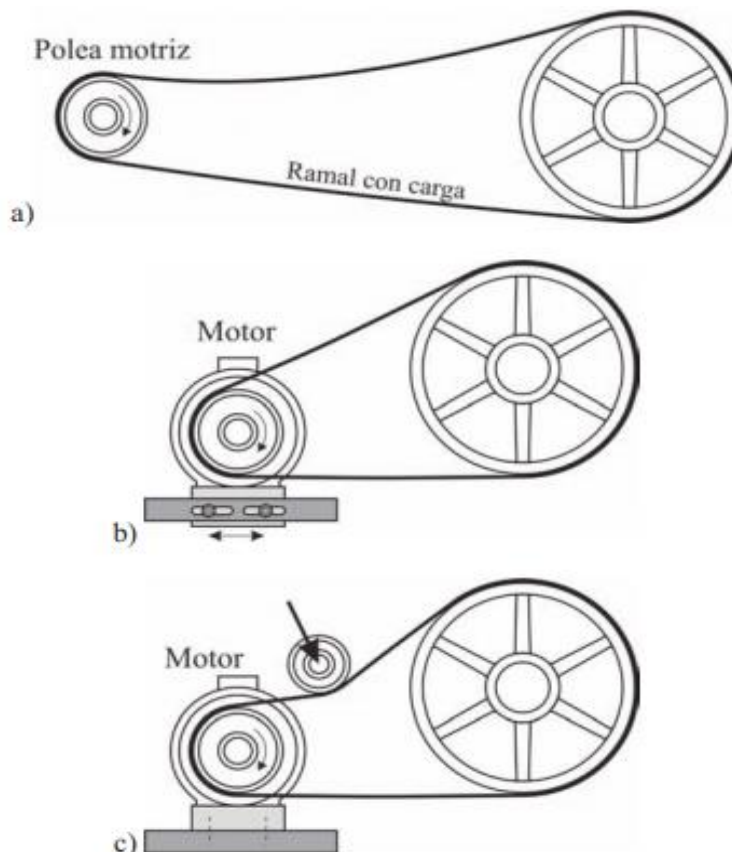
Distintos tipos de accionamiento en correas planas
